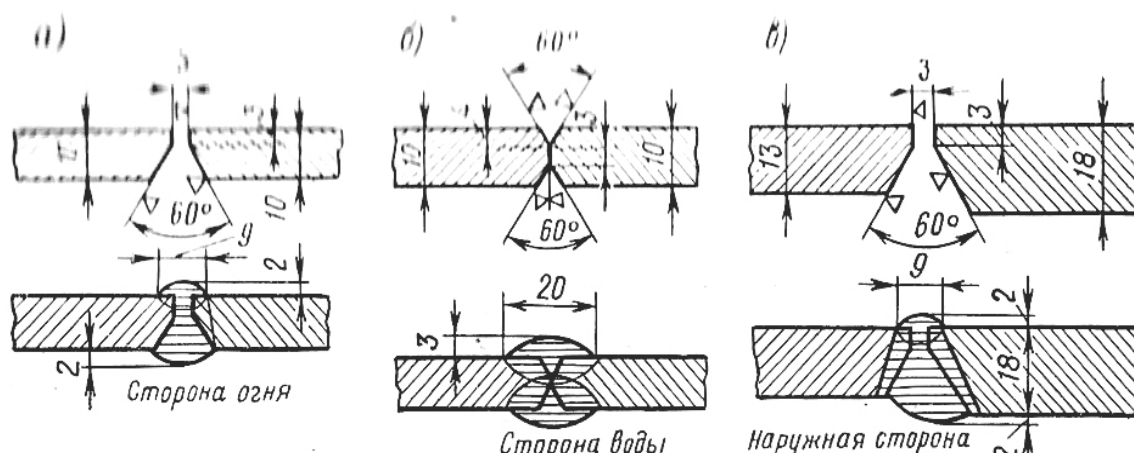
Подготовка стыков и наплавка сварочных швов:
